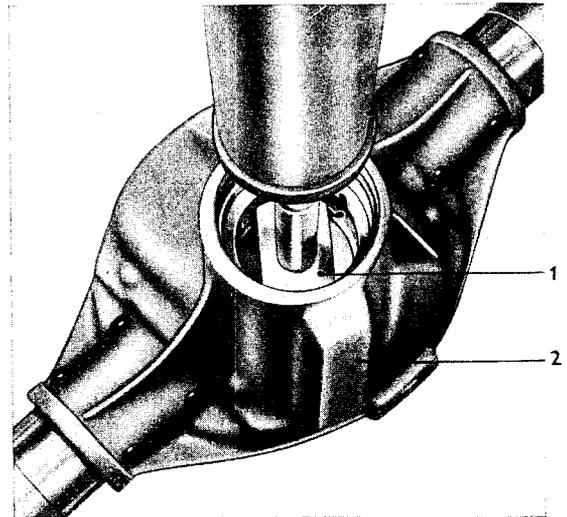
Äußeren Laufring des inneren Kegellagers aus Hinterachsgehäuse auspressen
